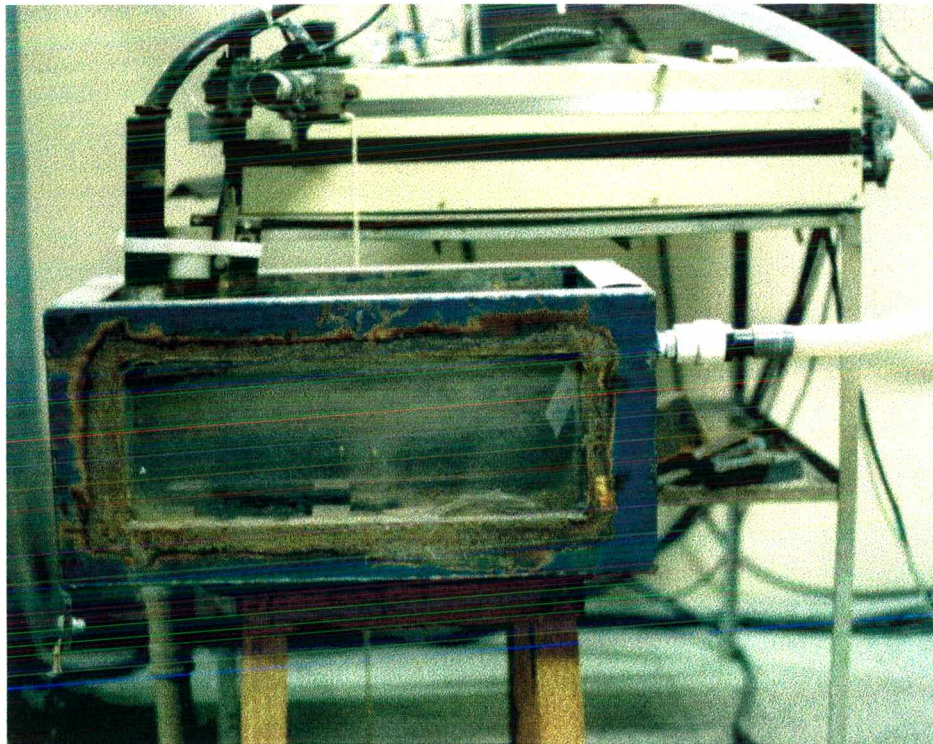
Vista geral da bancada para soldagem molhada.
